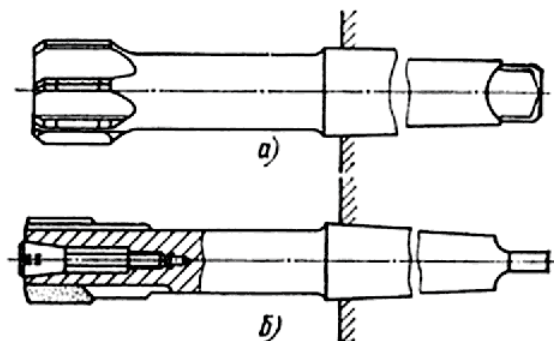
Типы разверток из быстрорежущей стали:
